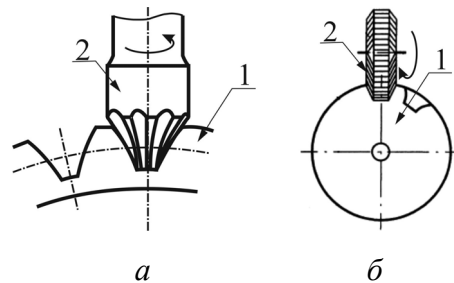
Нарезание зубчатого колеса методом копирования: пальцевой фрезой (а); дисковой фрезой (б)
